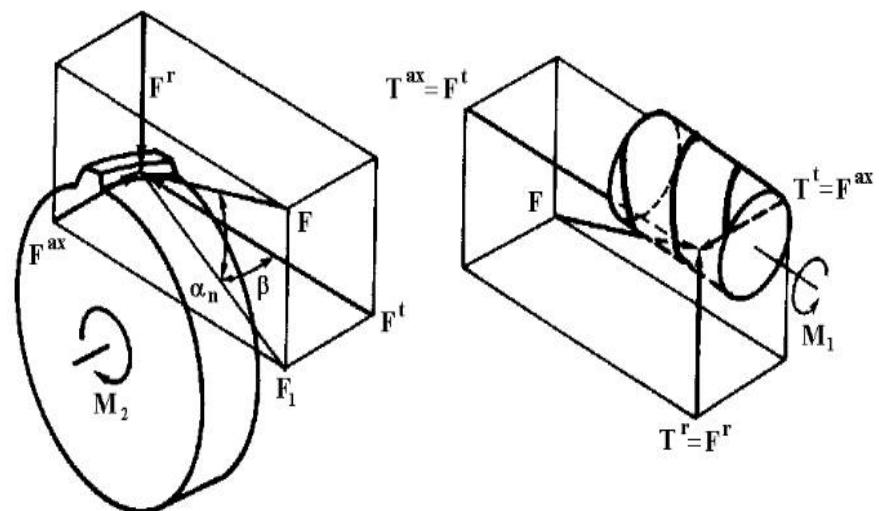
Fuerzas en un engranaje de tornillo sinfín
